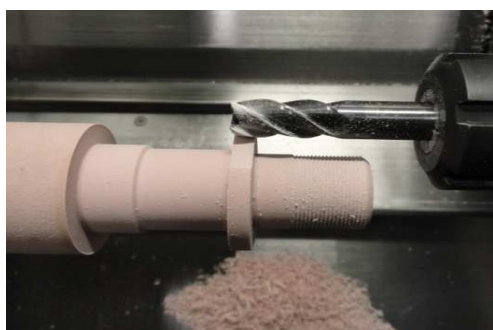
Hrubování  $\varnothing 28$  při realné výrobě
